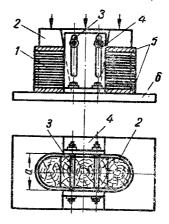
Приспособление для опрессовки катушек роторов с явио выражеииыми полюсами:
